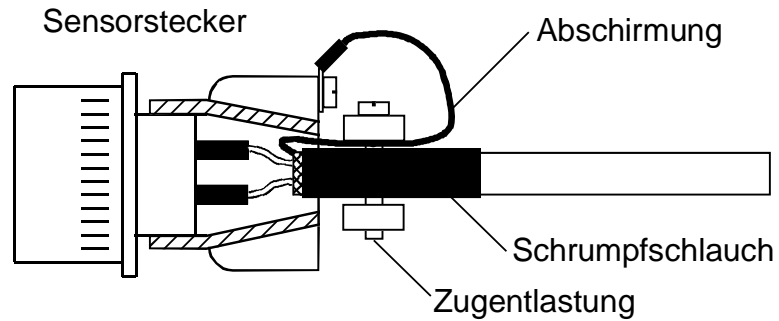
Beispiel einer Schirmbefestigung im Stecker
